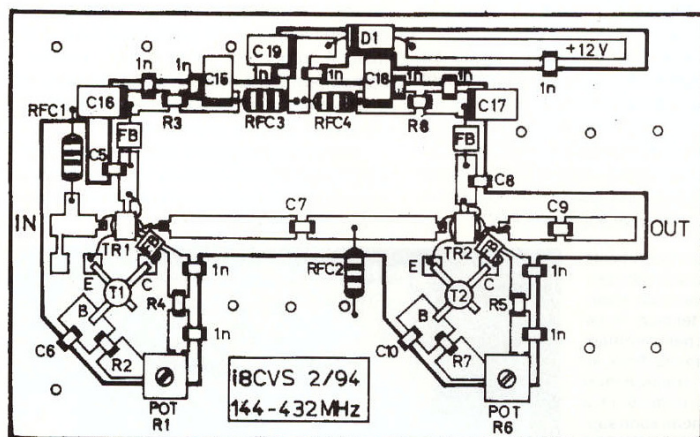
• Il PCB del preamplificatore con la disposizione fisica dei componenti
